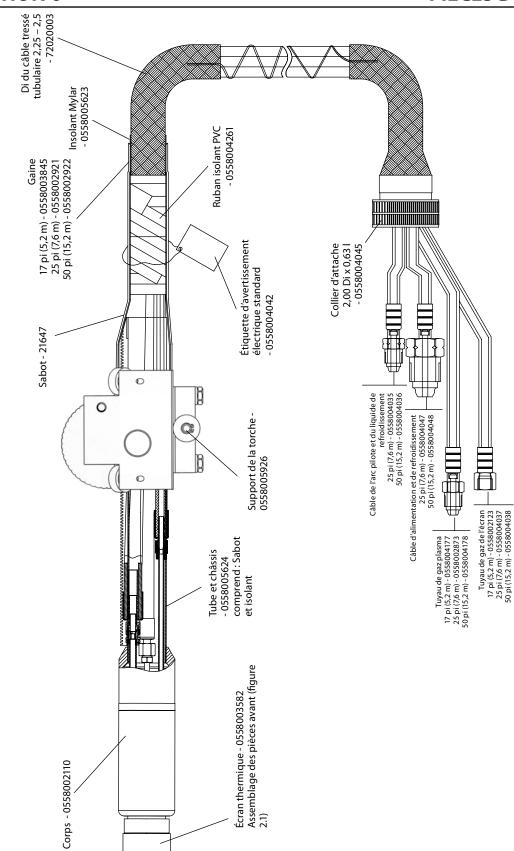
Pièces de rechange - ensemble de la torche PT-26 « SL » en ligne
